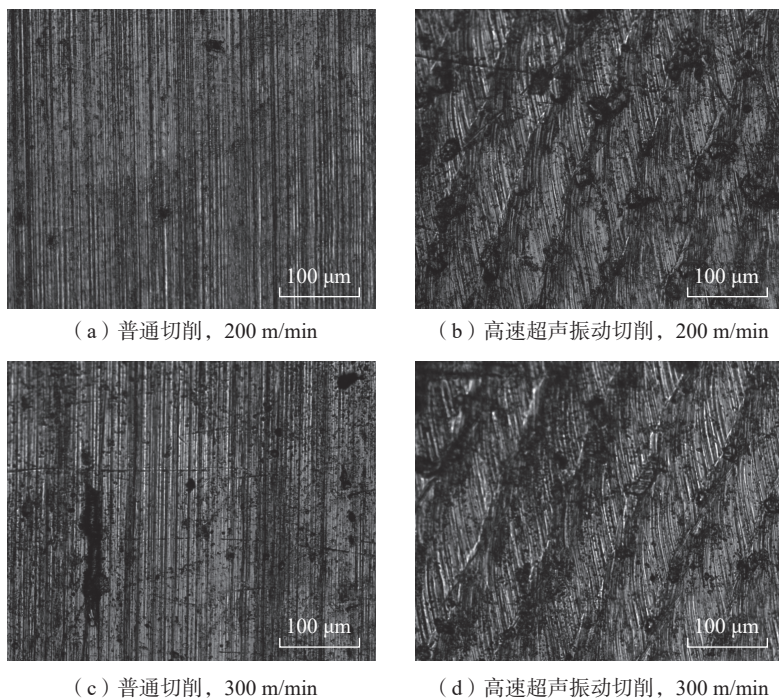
普通切削和高速超声振动切削加工获得的钛合金表面形貌
